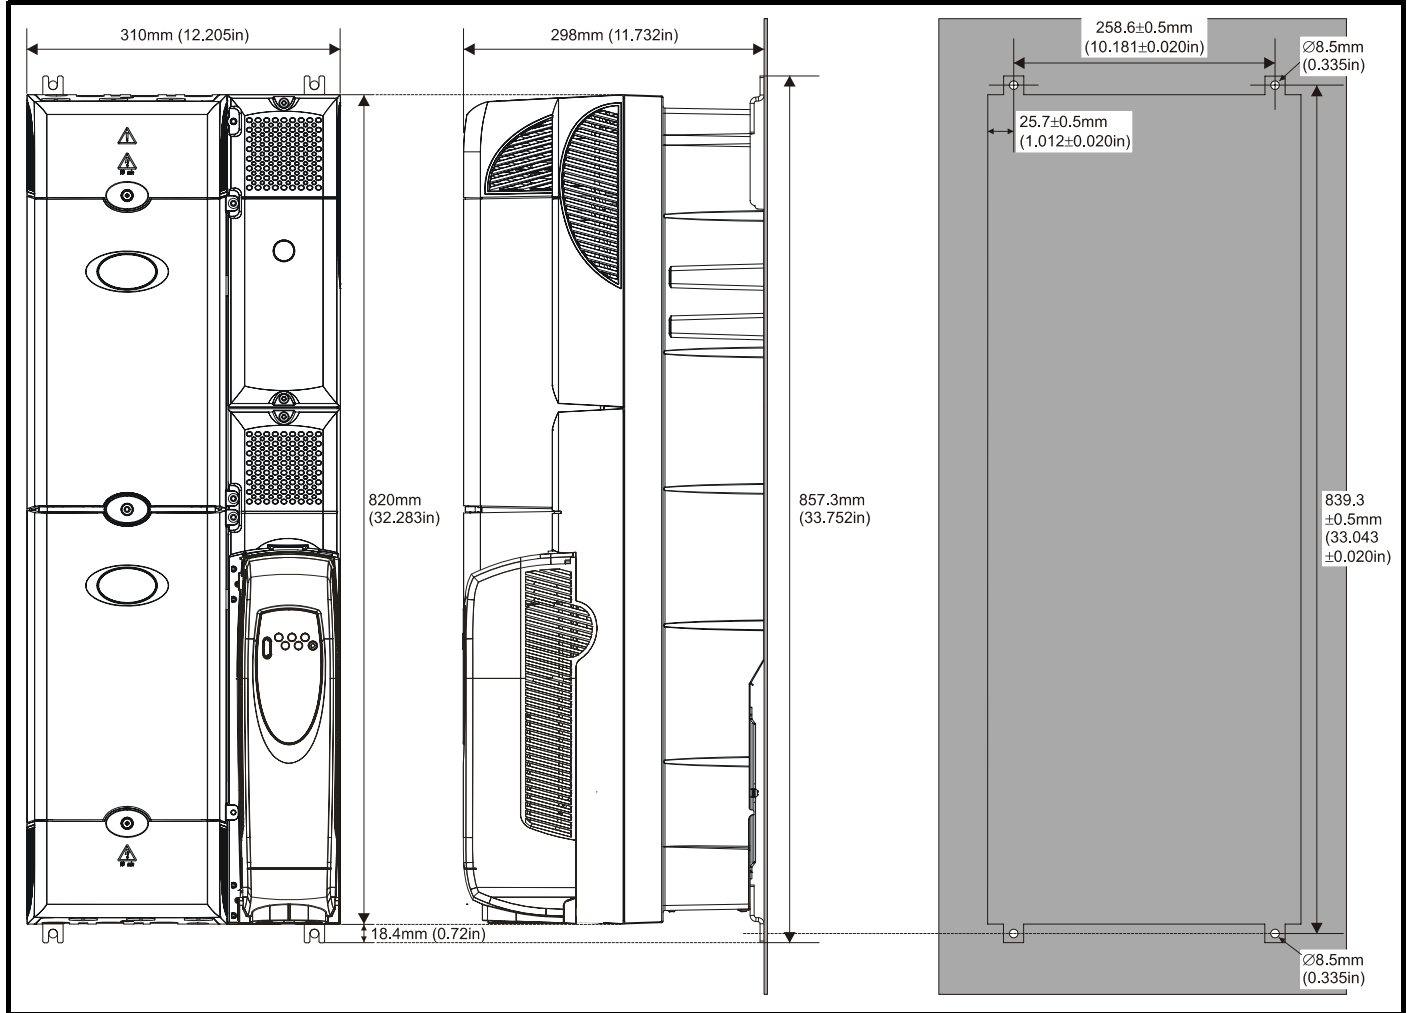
Boy 3 sürücülerin yüzey montajı
